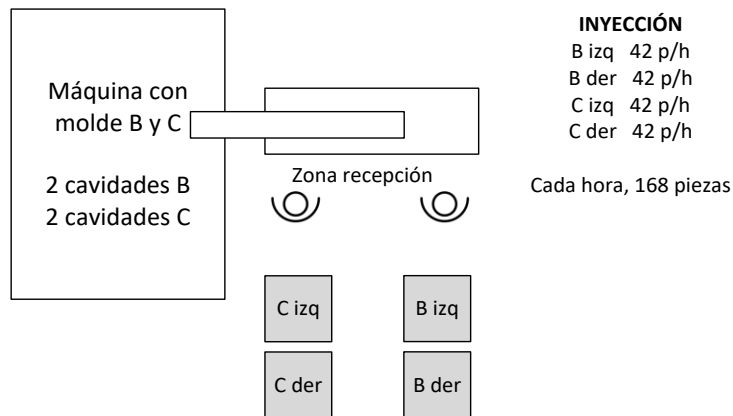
1 Layout del proceso de inyección del conjunto B y C
